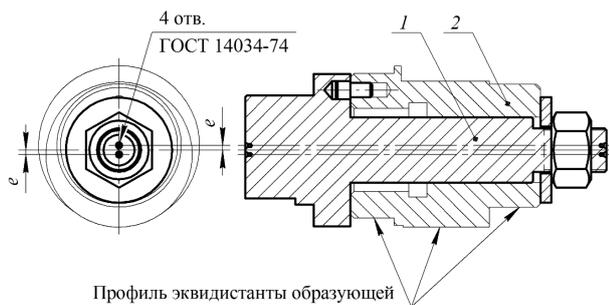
Технологическая оснастка для изготовления генератора волн: 1 – оправка со смещенными на  $180^\circ$  центровыми отверстиями; 2 – генератор волн 4-рядного редуктора
